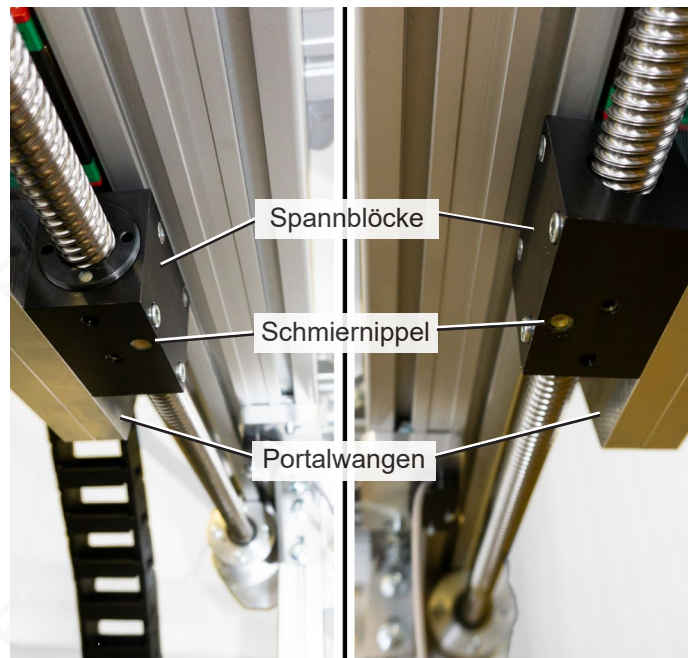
Von unten fotografierte linke und rechte Außenspindel einer Gantry-Maschine. Spindelmuttern gegensinnig montiert, damit beide Schmiernippel nach unten weisen.
